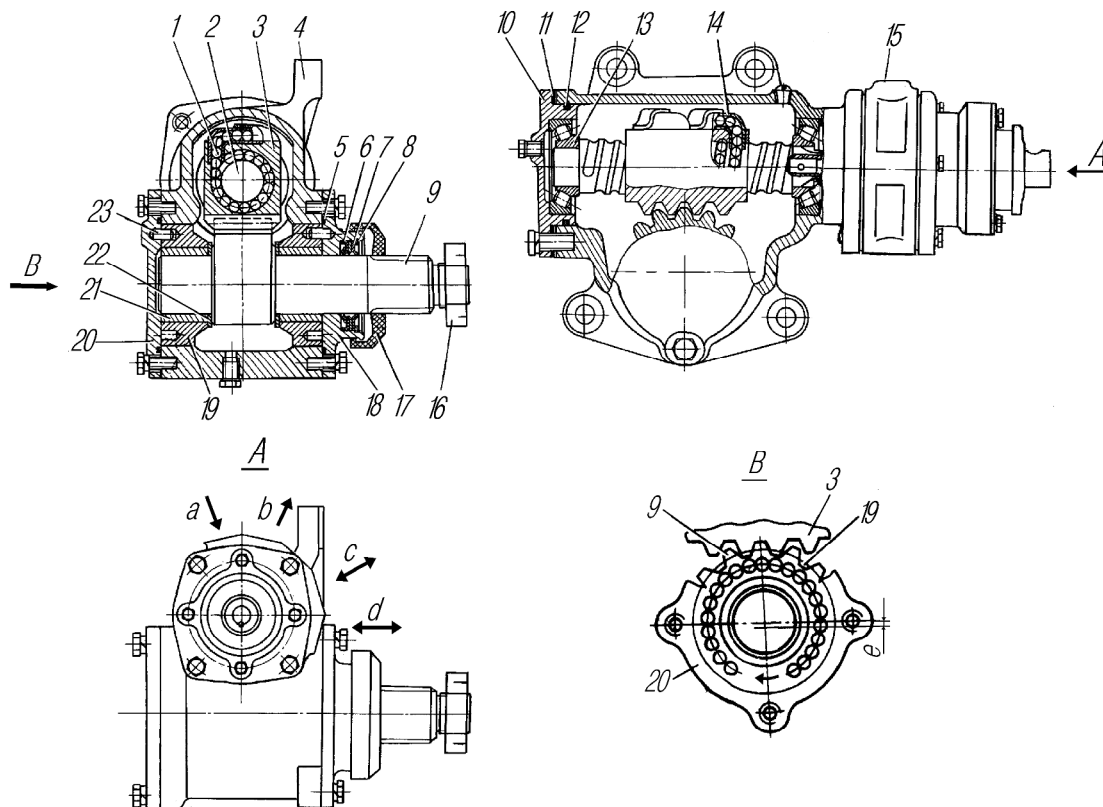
Механизм рулевой (винт- шариковая гайка- рейка- сектор):
